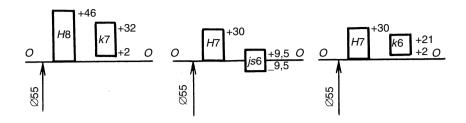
Схемы расположения полей допусков различных вариантов посадок червячного колеса на вал (со шпонкой)
